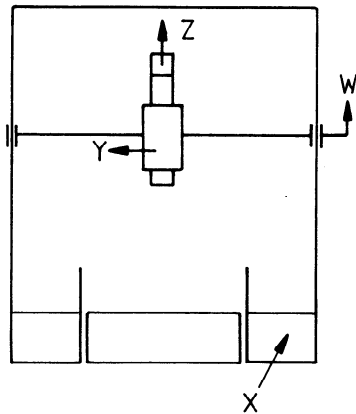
Type 1: Machine à une tête de fraisage sur traverse mobile
